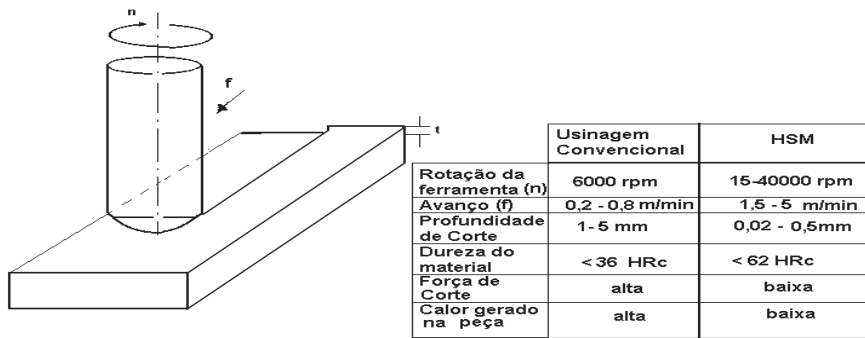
Diferença entre a usinagem convencional de ferramentas e a usinagem ultra-rápida (HSM) /7/.
